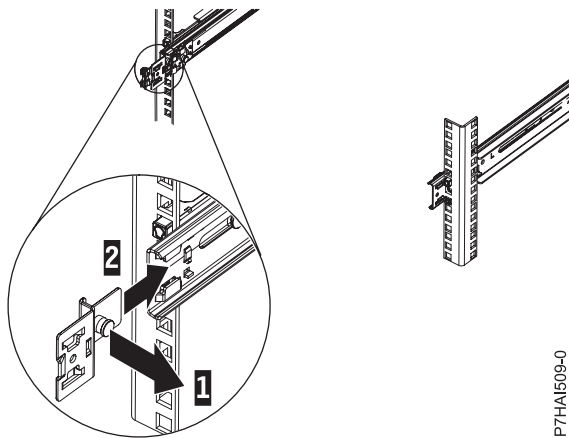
Pino do Suporte de Montagem Estendido e Suporte de Montagem Instalado no Trilho Deslizante
